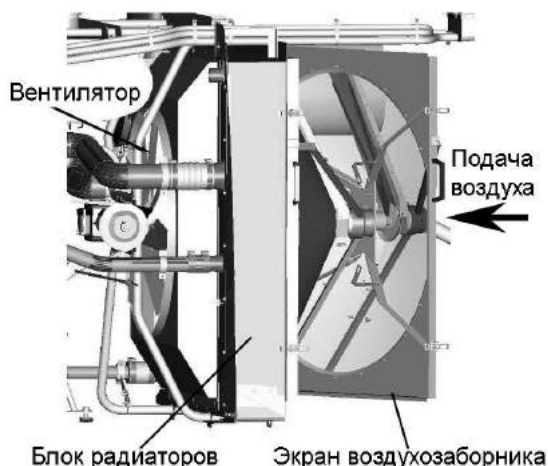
Обдувка сжатым воздухом блока радиаторов
